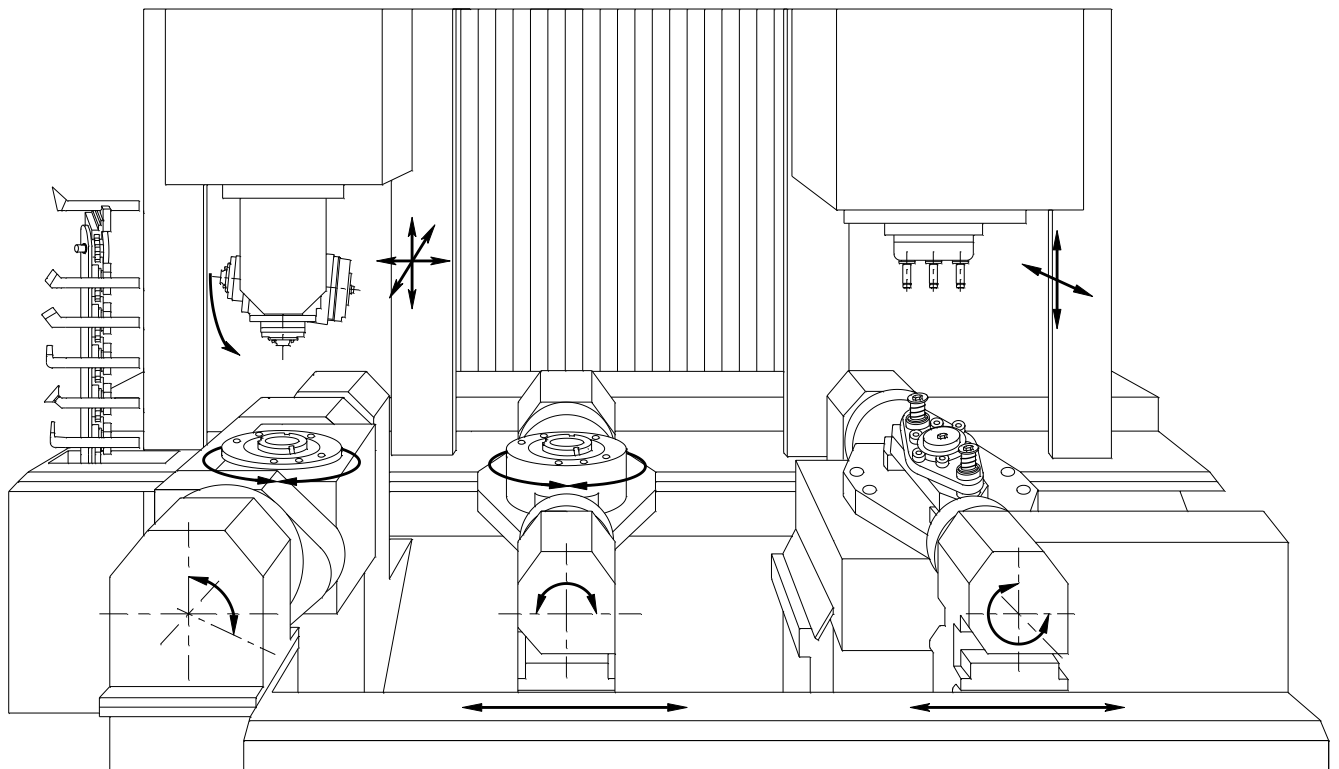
Схема компоновки оброблювального центру ОВМ21
